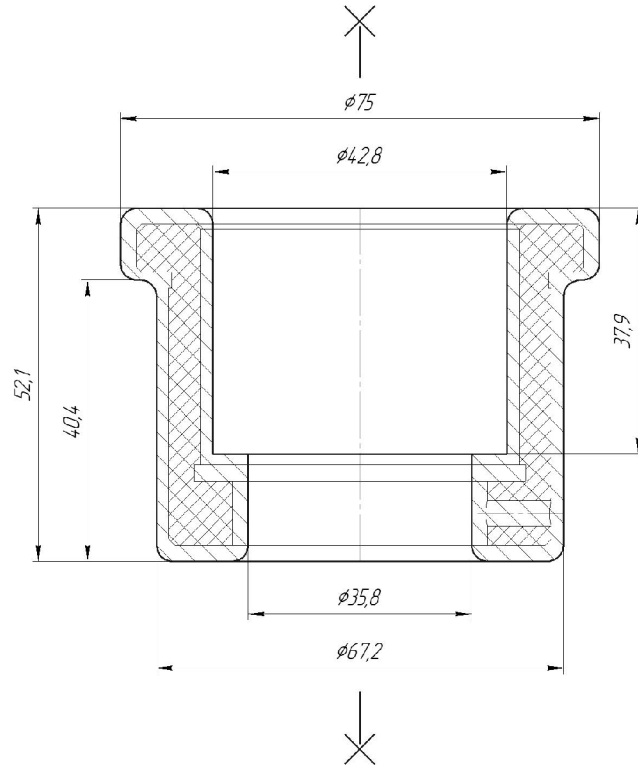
Ескіз заготовки, отриманої литтям в облицьований кокіль
